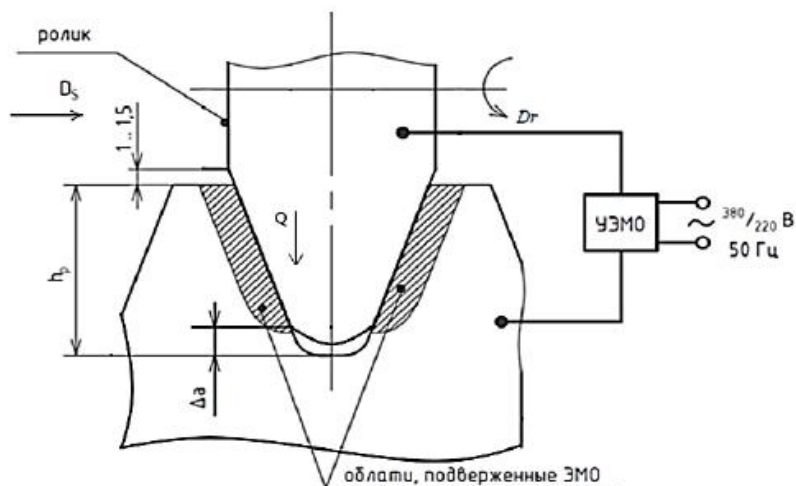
Схема ЭМО резьбы корпуса УЭЦН
